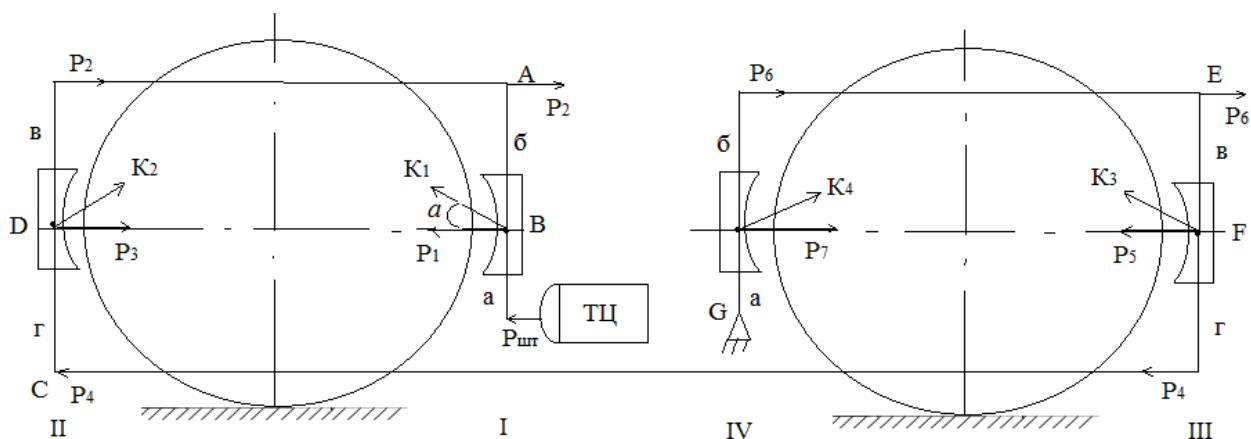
Предлагаемая компоновка ТРП грузового вагона с нажатием колодок на колесо с двух сторон и одним тормозным цилиндром
